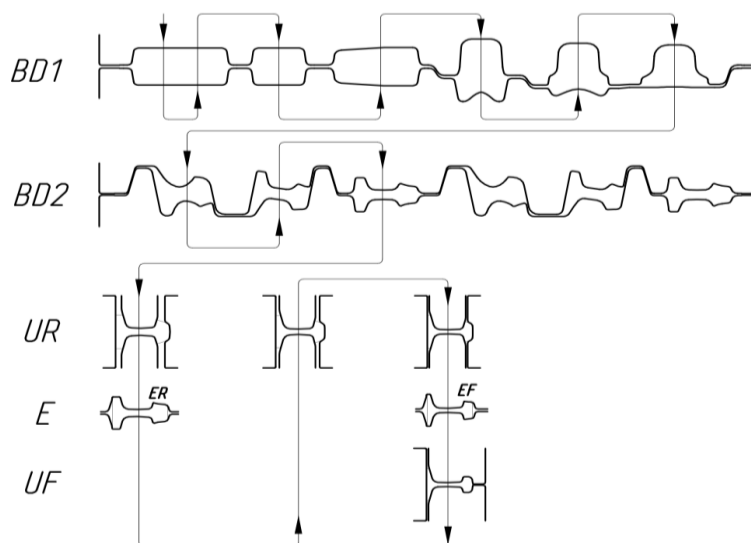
Схема прокатки рельсов с разрезкой заготовки в трапецевидном калибре
